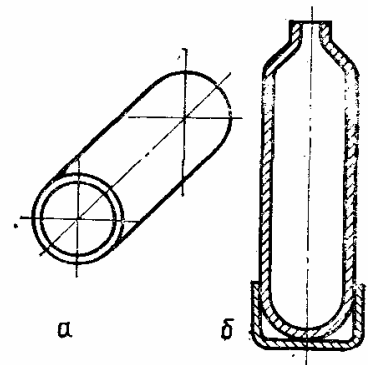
Оболочки: *a* — цилиндрическая оболочка (корпус двигателя); *б* — оболочка сосуда высокого давления
